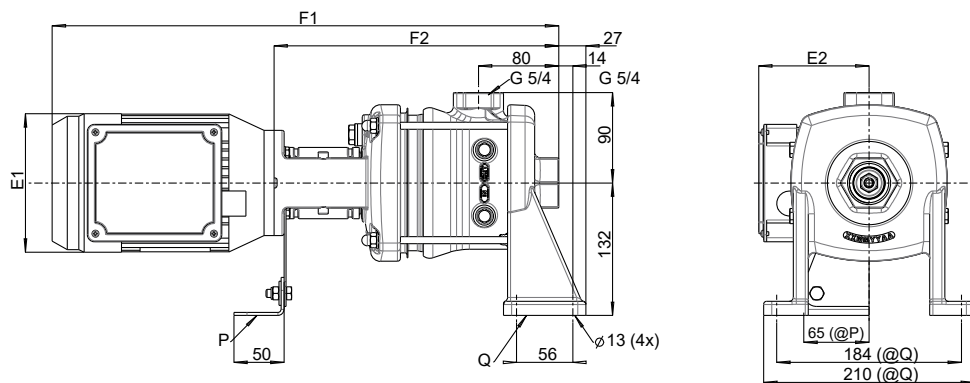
Abmessungen und Anschlüsse Movitec H(S)I 6 mit Motor V18¹³⁾
